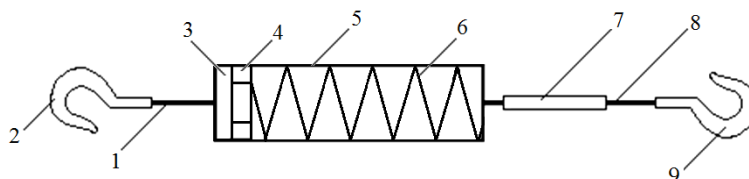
Пристрій для закріплення несучої конструкції вагона на палубі залізничного порому
